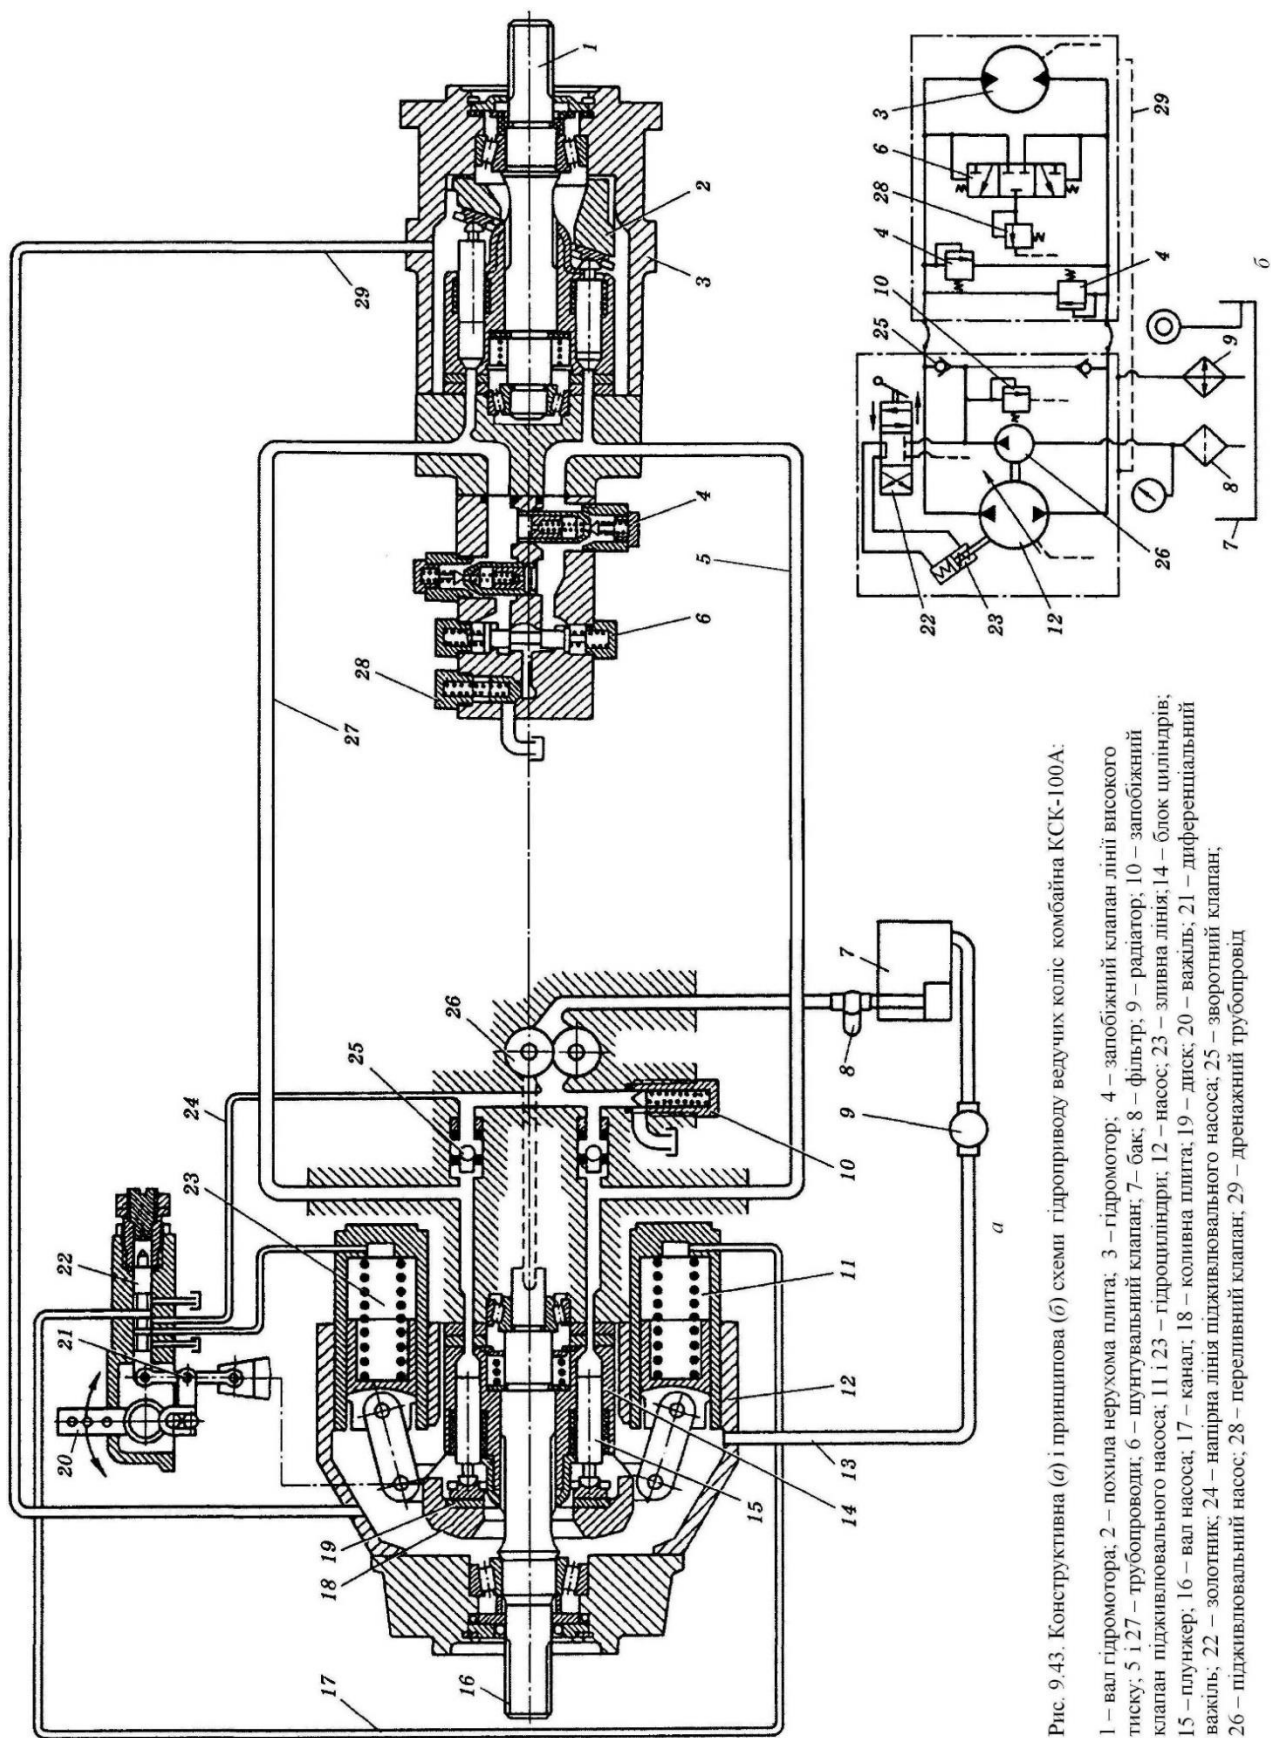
Конструктивна (а) і принципова (б) схеми гідроприводу ведучих коліс комбайна КСК-100А:
